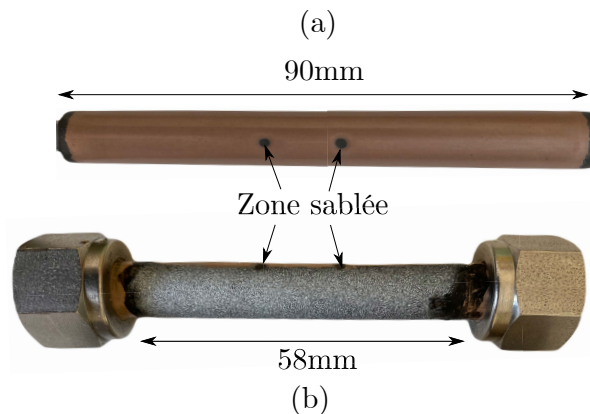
Éprouvette avec (b) et sans (a) les raccords Swagelock sertis et le mouchetis. La couche de pré-oxyde est localement retirée par sablage pour permettre la soudure des thermocouples.
